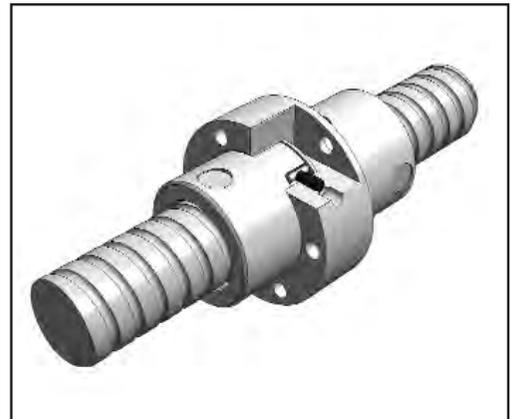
Flanschmutter mit Vorspannvorrichtung
